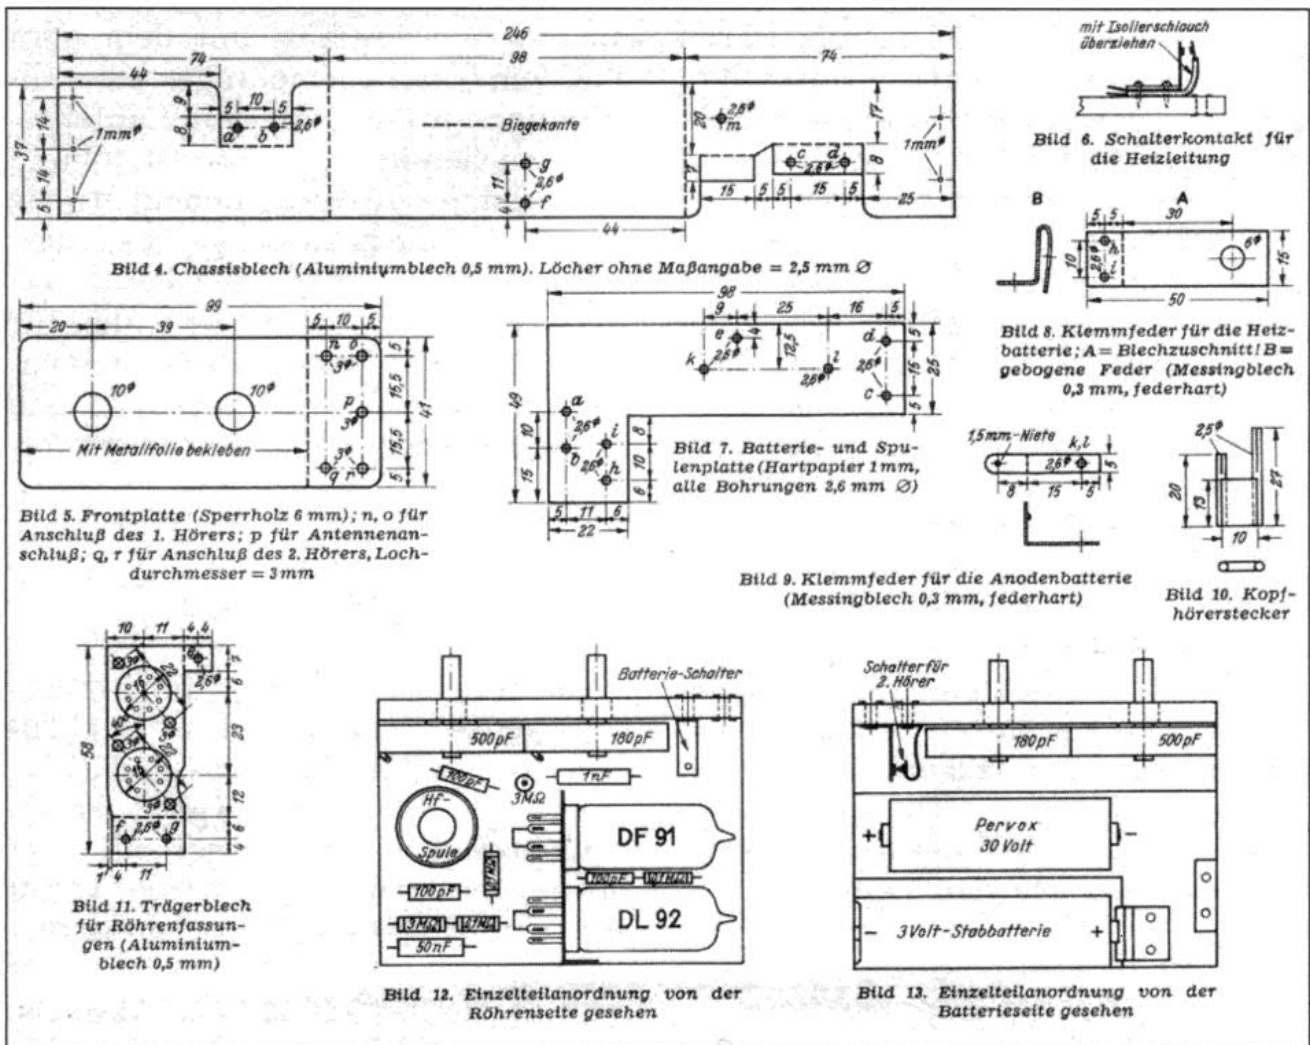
Liebe zum Detail: K. SAUERBECK lieferte präzise Konstruktionszeichnungen zu seinen Bauanleitungen (aus Funkschau 1/1953).
